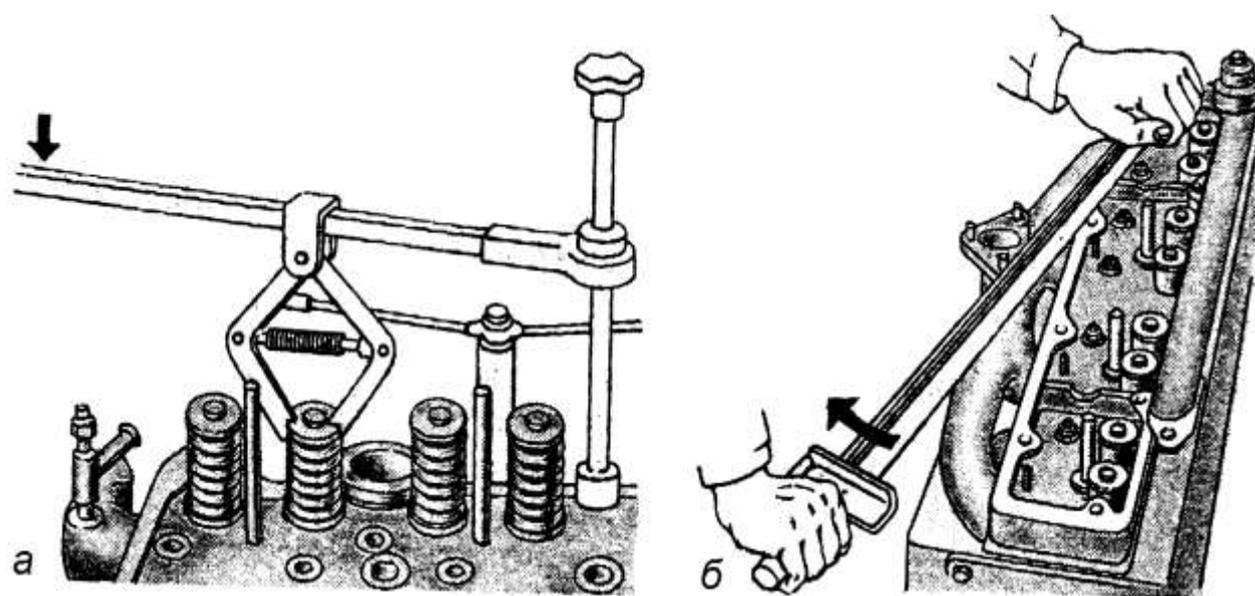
Приспособление для разборки и сборки клапанного механизма:
